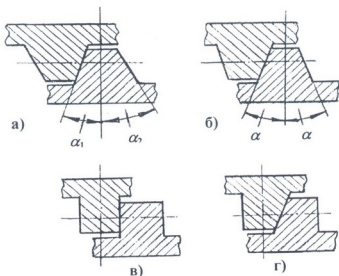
Профили зубьев в цилиндрических сечениях Б-Б зубчатых колес
